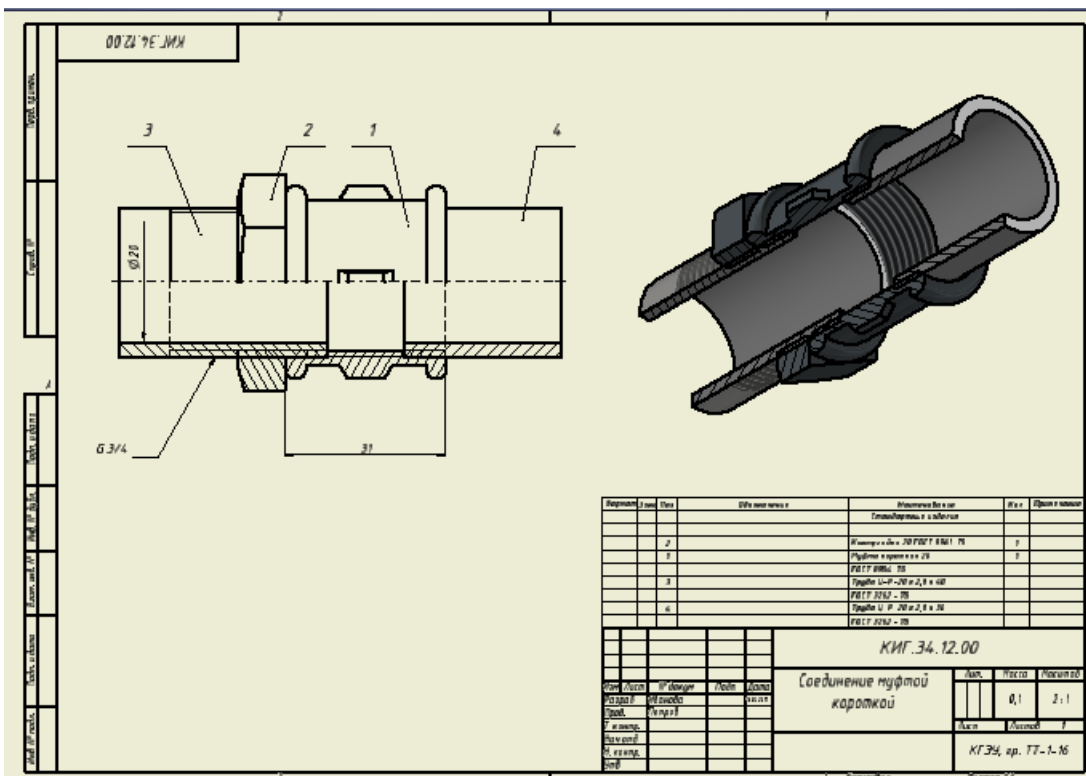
Чертеж соединения муфтой короткой со спецификацией на поле чертежа
